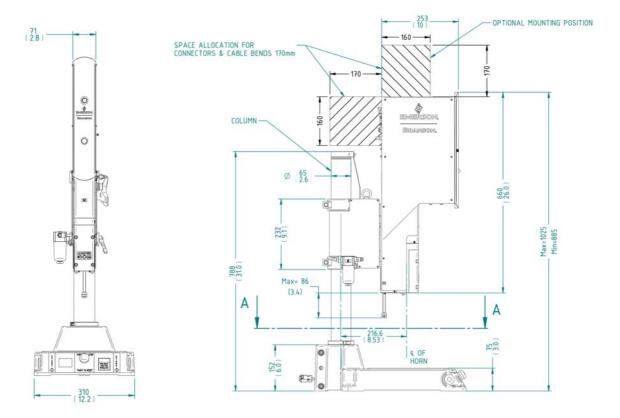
Габаритный чертеж привода 2000Хс
